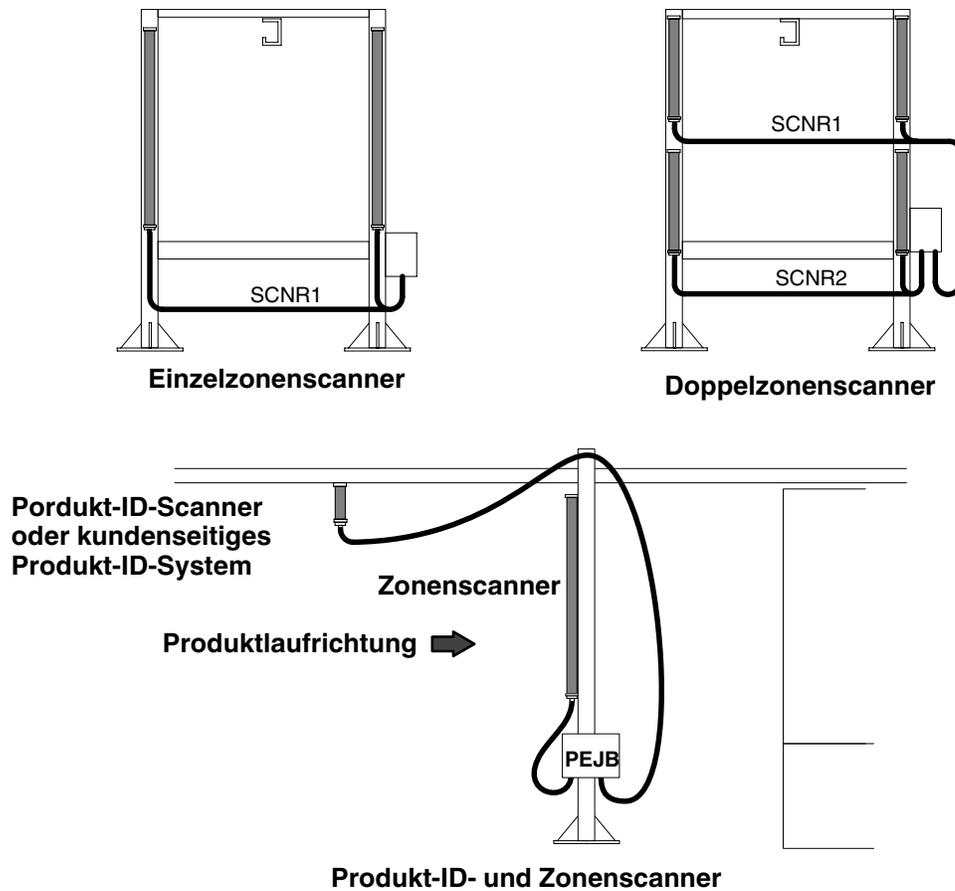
Kabelanschlüsse für Zonen- und Produkt-ID-Scanner
